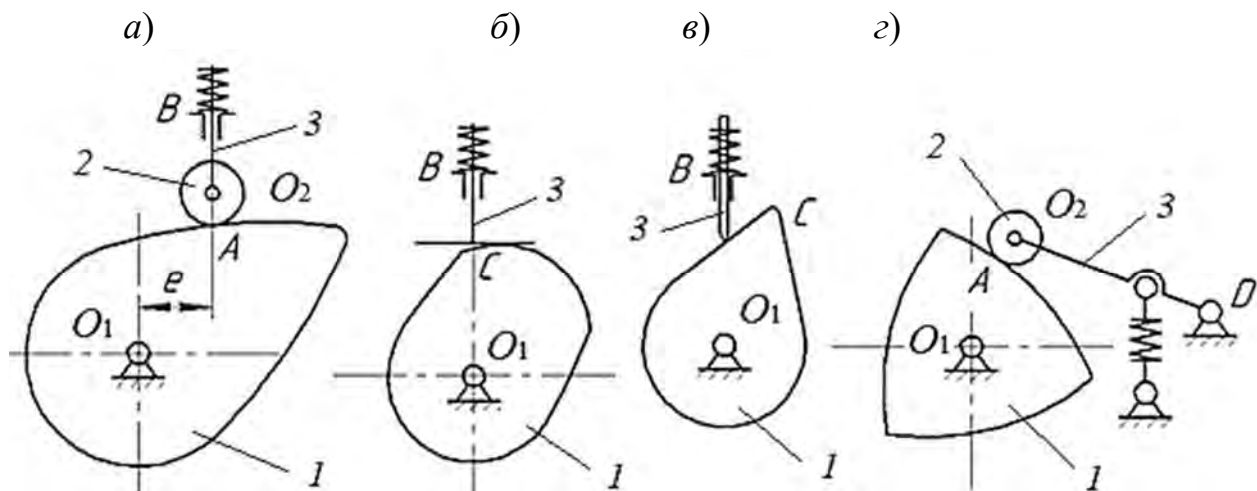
Кинематические схемы кулачковых механизмов: a – дезаксиальный кулачковый механизм с роликовым толкателем; $б$ – центральный кулачковый механизм с плоским толкателем; $в$ – центральный кулачковый механизм с игольчатым толкателем; z – кулачковый механизм с роликовым колебателем
